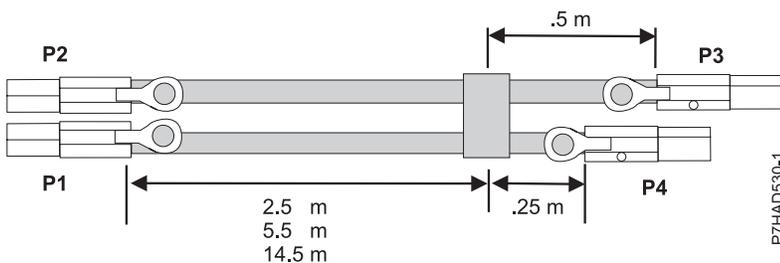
Comprimentos de Conjunto de Cabos do Cabo SAS X Externo
